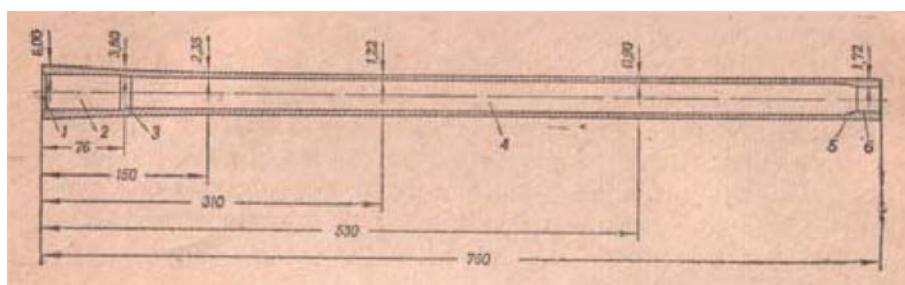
Типичная конструкция и размеры стенок ствола современного дробового двухствольного ружья: 1 - выемка под шляпку гильзы; 2 - патронник; 3 - снарядный вход (скат из патронника в ствол - переходный конус); 4 - канал ствола; 5 - чоковое сужение; 6 - канал чока
